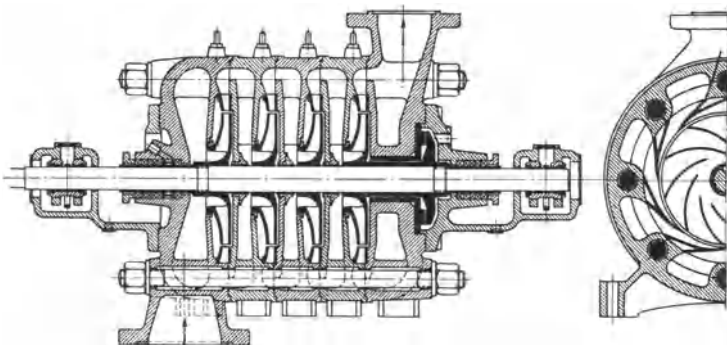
Kesselspeisepumpe. C. H. Jaeger & Co., Leipzig.
